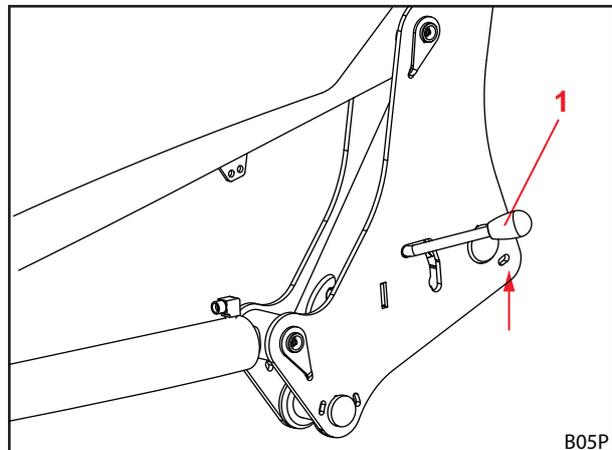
Apertura del dispositivo di blocco del caricatore frontale
